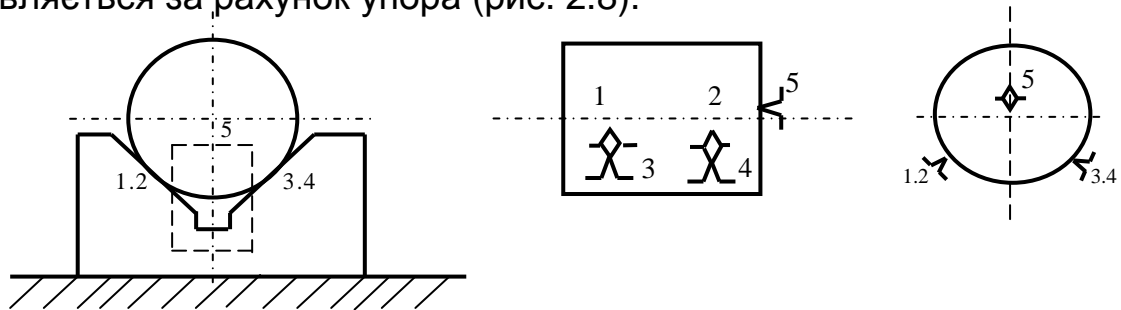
Схема базування циліндричної заготовки в призмі
